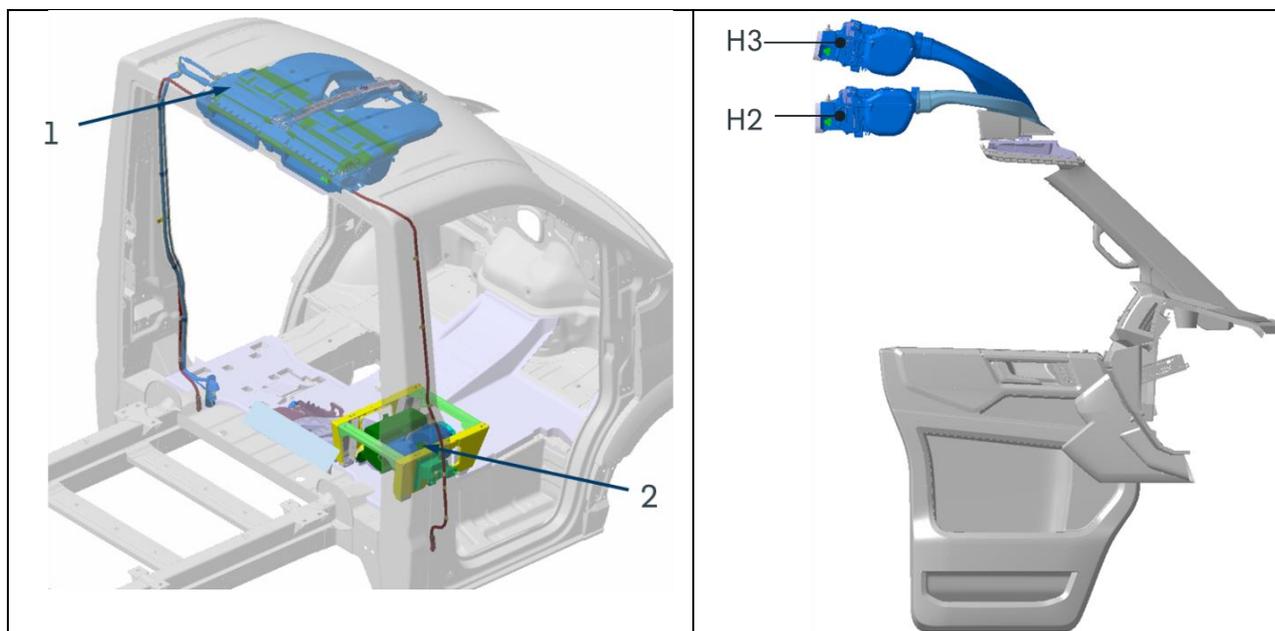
posizione di montaggio dei singoli componenti nella cabina di guida (vista dall'alto e vista in sezione per tetto di diverse altezze)
